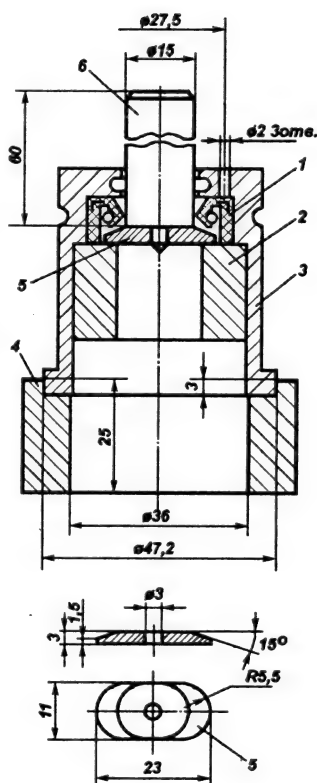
Приспособление для выпрессовки сальника и втулки из стакана редуктора
